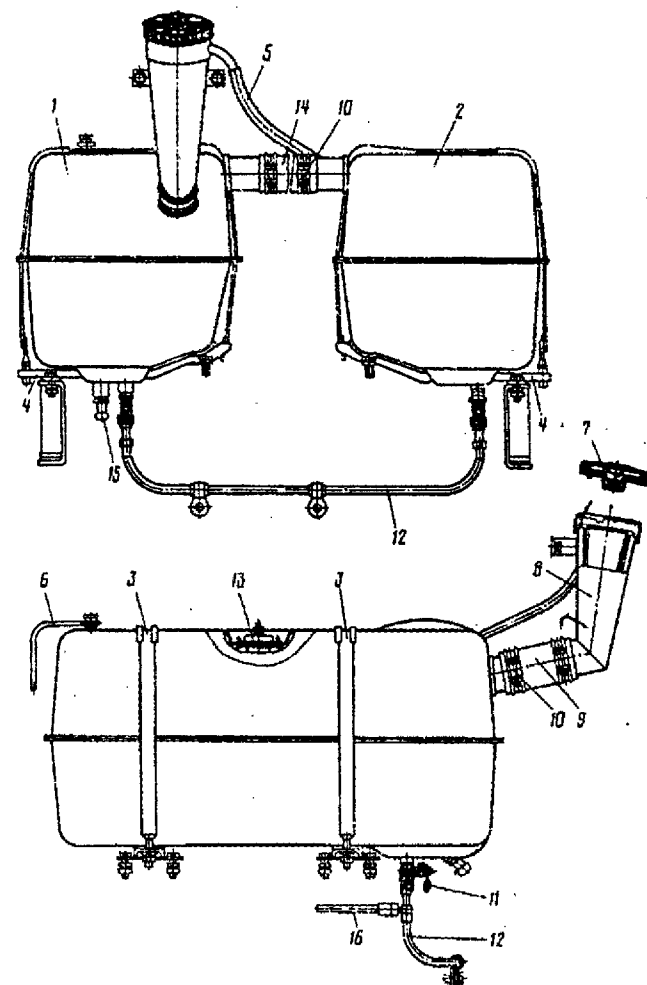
Топливный бак дизеля (МТЗ-100, МТЗ-102). 1 - левый бак; 2 - правый бак; 3 - стяжная лента; 4 - кронштейн топливного бака; 5 - дренажная трубка; 6 - топливоотводящая трубка от форсунок; 7 - крышка заливной горловины; 8 - заливная горловина; 9 - соединительный рукав заливной горловины; 10 - стяжной хомут; 11 - заборный кран; 12 - соединительный трубопровод; 13 - датчик топливомера; 14 - соединительный рукав топливных баков; 15 - сливной кран; 16 - расходный топливопровод
